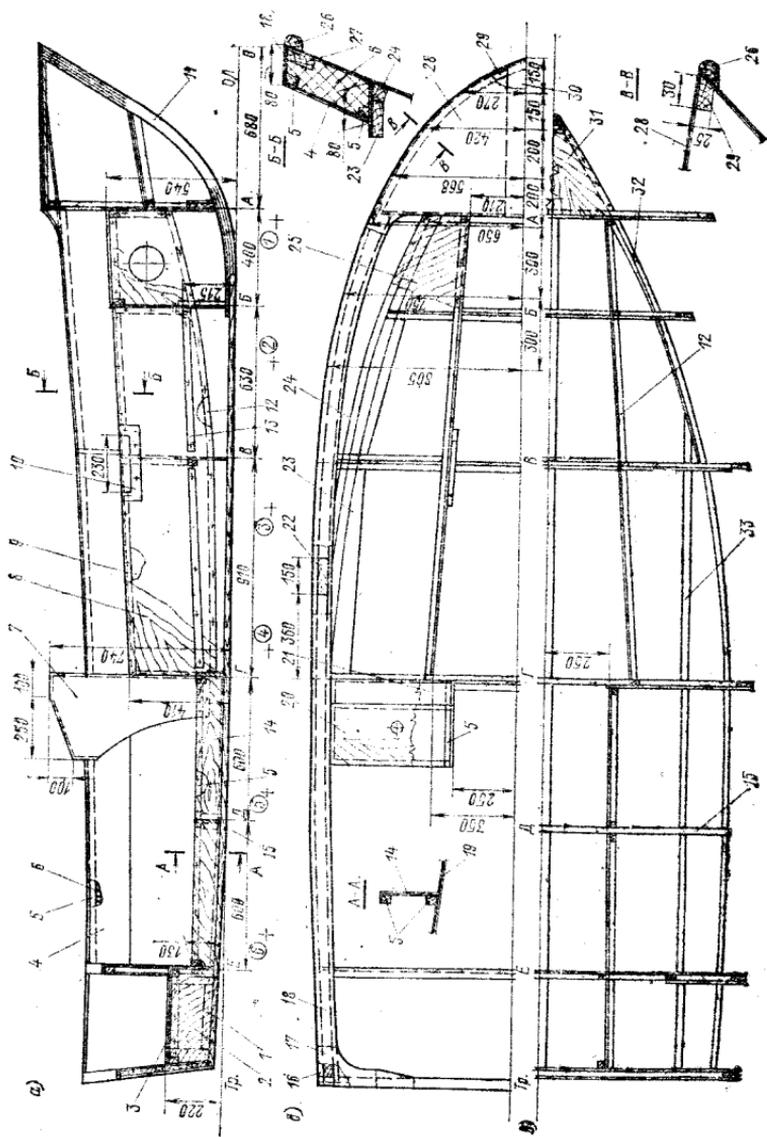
Конструктивный продольный разрез корпуса (а), вид сверху на набор (б) и на набор днища (в)
